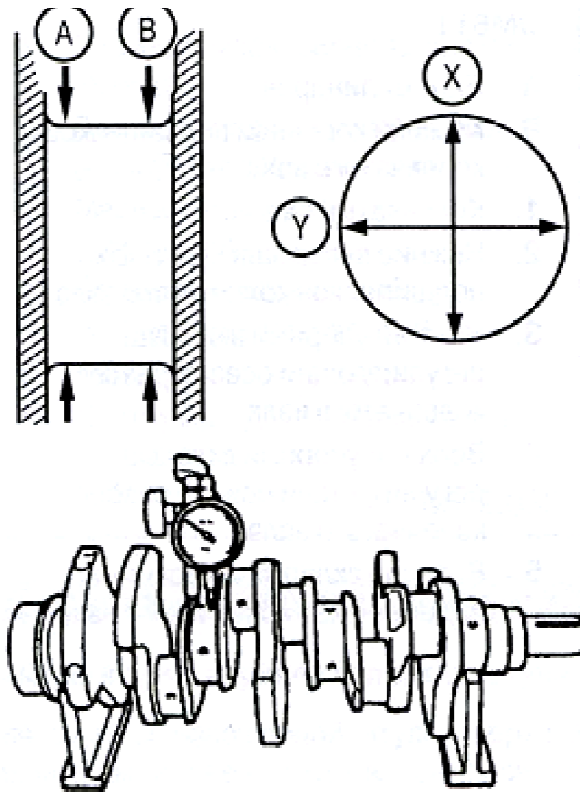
Схема вимірювання шийок колінчатого валу
